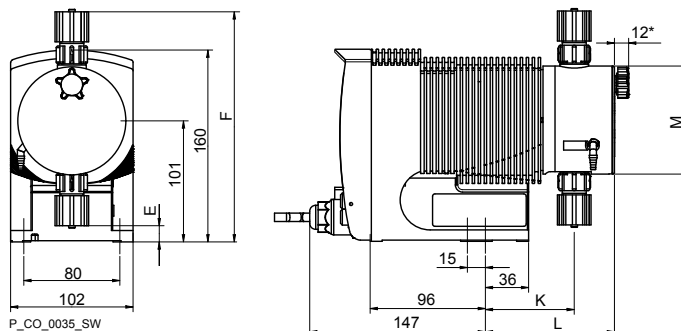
Габаритный чертеж Concept L, исполнения из материала PPE, PPB - размеры в мм
